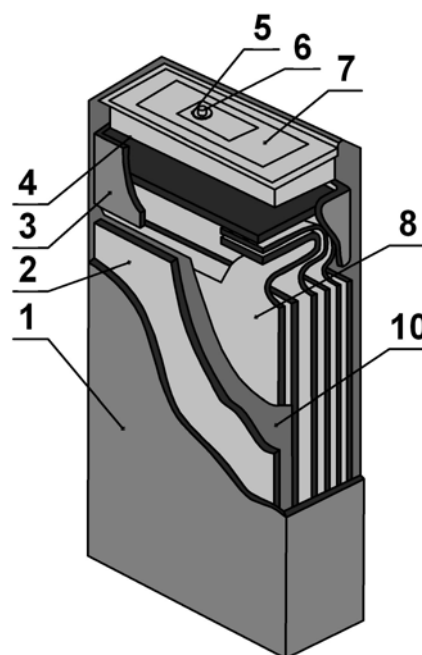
Конструкция Ni-MH аккумулятора: 1-корпус; 2 - отрицательный электрод; 3 - изолятор; 4 - изоляционная прокладка; 5 - колпачок клапана; 6 - датчик давления; 7 - крышка; 8 - положительный электрод; 9 - сепаратор
